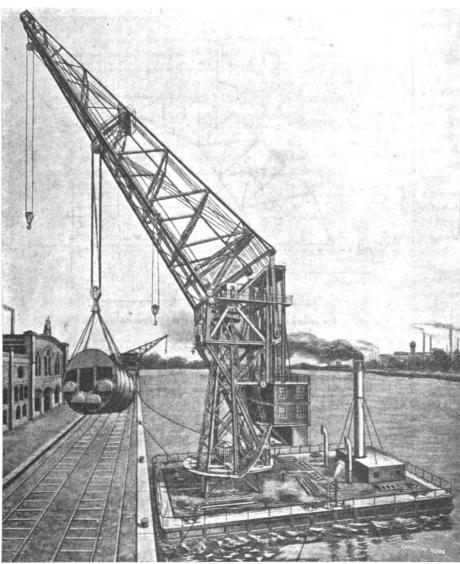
Gru galleggiante da 150 tonn. dei Cantieri di Kiel - Vista.
